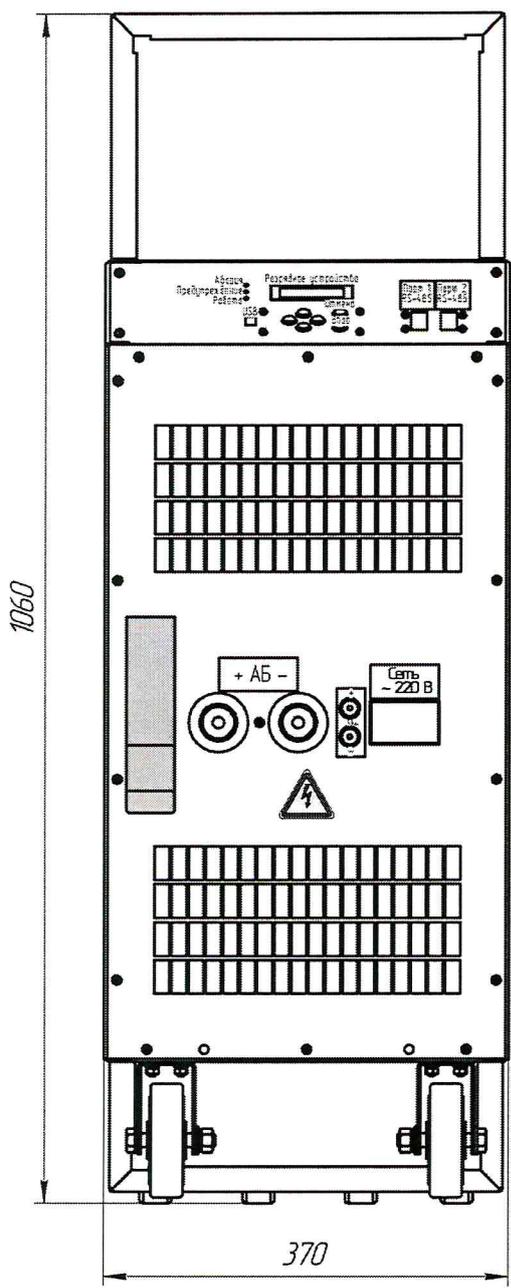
Общий вид и габаритные размеры СКР-100
